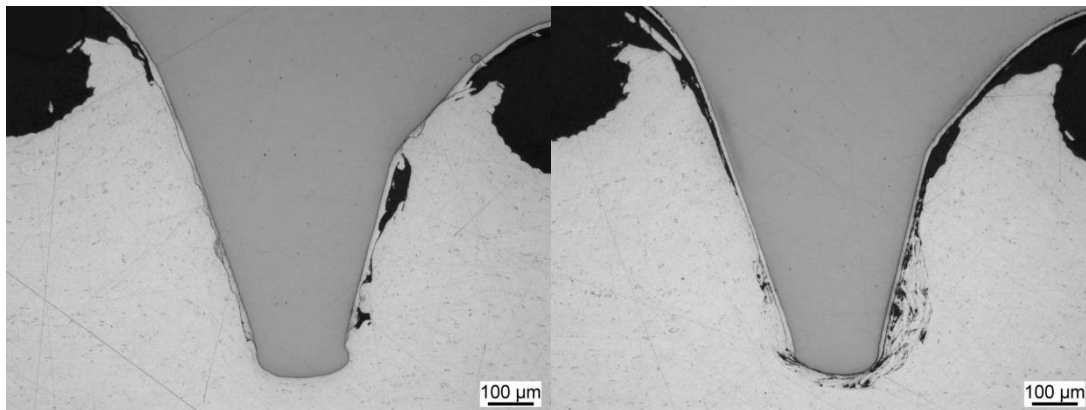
Gewindekontakt, Verschweißungen und Verschleiß beim Gewindefurchen am Beispiel von Variante S8-9 (ALtracs® Plus) für den Vorlochdurchmesser $DVL = 7,2 \text{ mm}$ in EN AW-6082 T6 [1]
